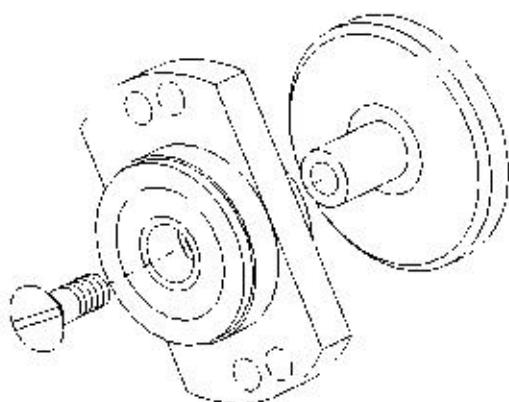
Сборка фланцевого планетарного держателя шлифовального шпинделя
